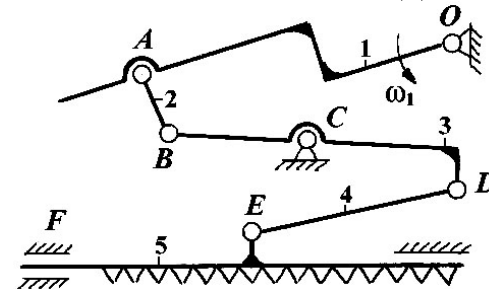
Механизм привода режущего аппарата жаток кормоуборочного комбайна КСК-100
